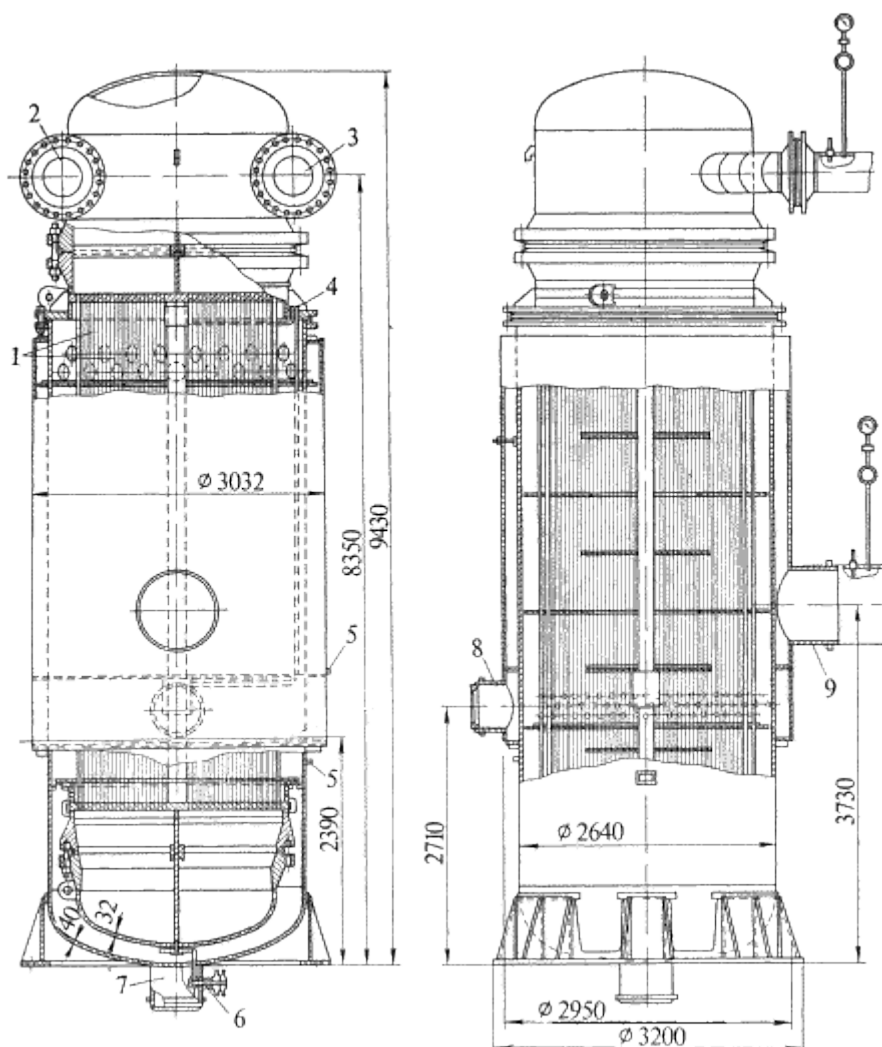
Конструкция подогревателя низкого давления поверхностного типа
